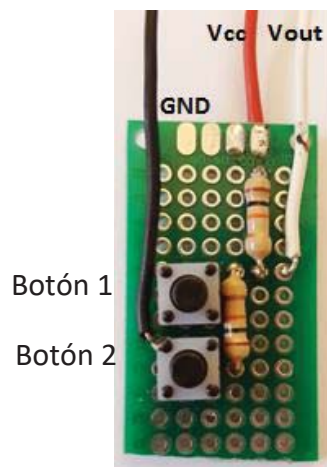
Botonera soldada en un PCB estándar perforado
